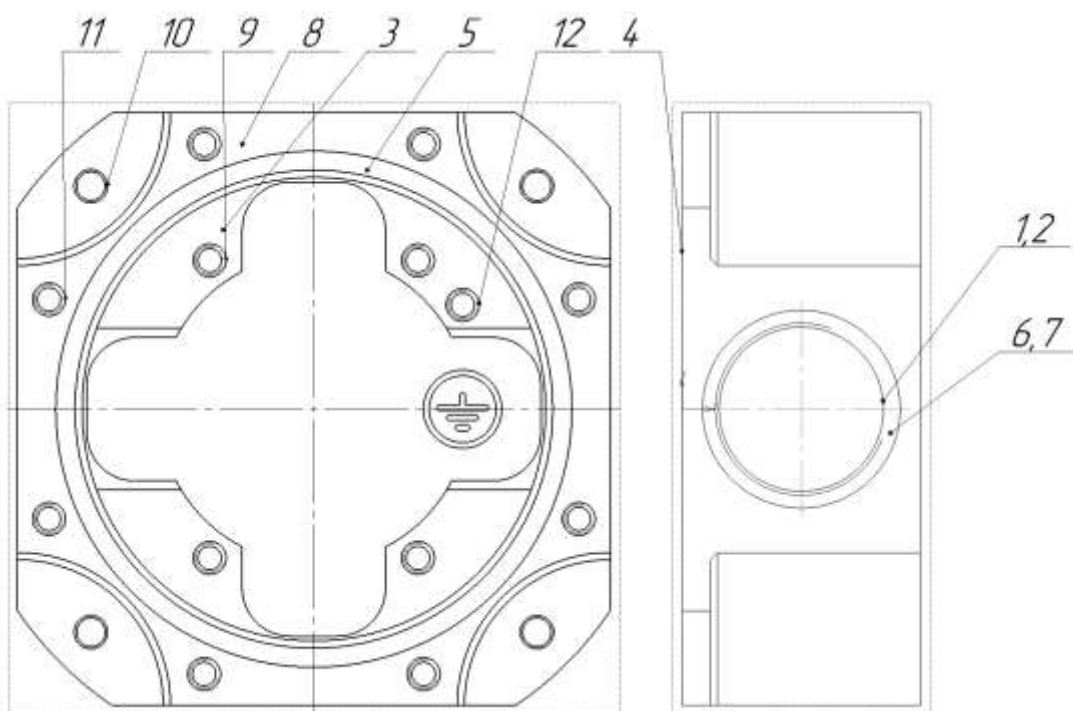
До визначення функцій поверхонь корпусу клемної коробки
